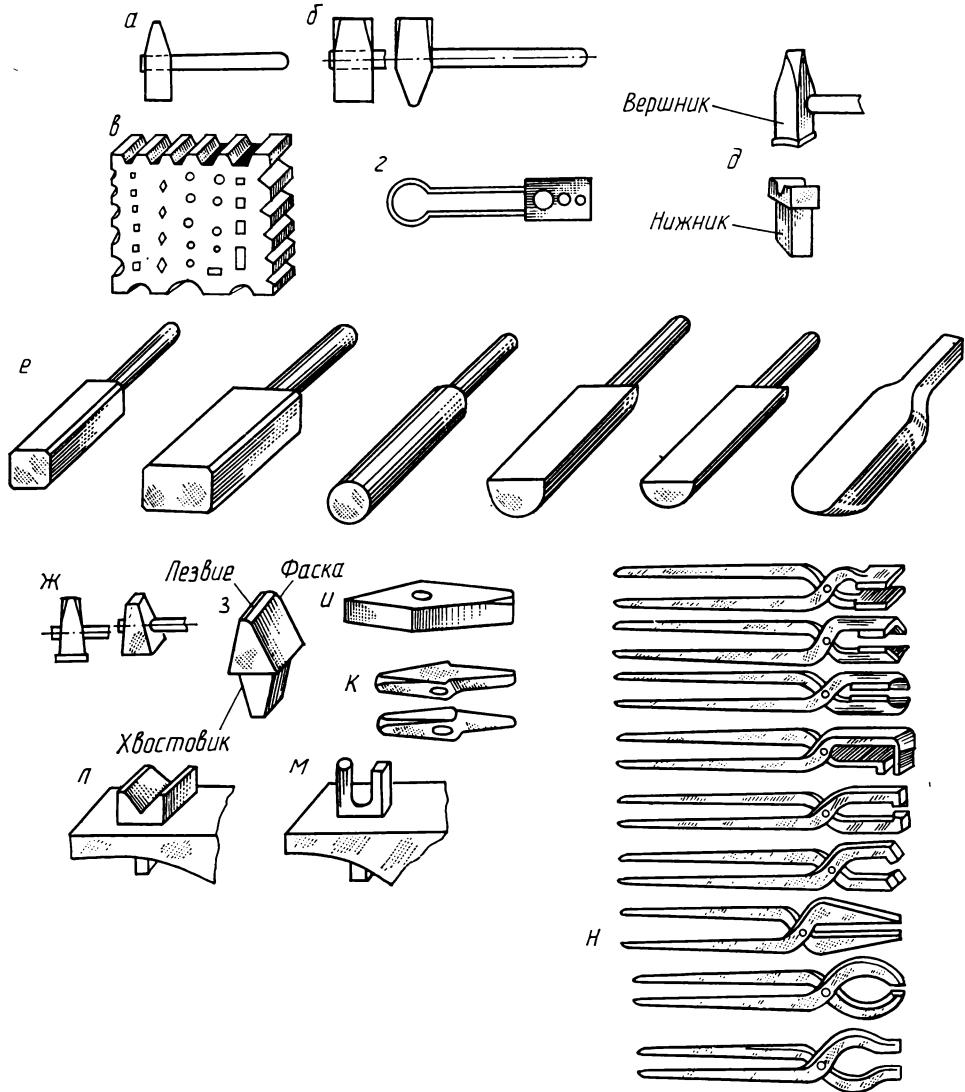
Инструменты и приспособления для свободной ручной ковки:
